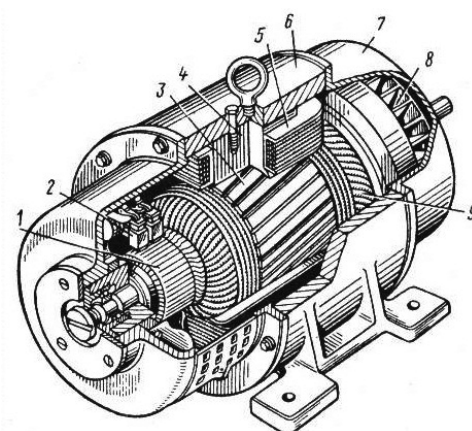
Типовая конструкция ЭДПТ: 1 – коллектор; 2 – щеточный контакт; 3 – сердечник якоря; 4 – сердечник индуктора (полюса); 5 – обмотка возбуждения; 6 – корпус; 7 – крышка вентилятора; 8 – вентилятор; 9 – обмотка якоря
